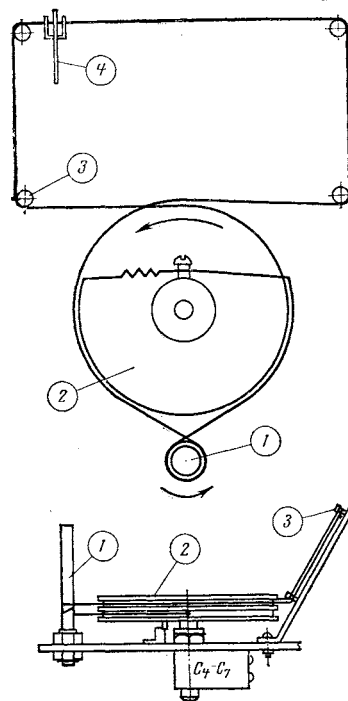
Кинематическая схема верньерного устройства: 1 — ось настройки; 2 — маховик; 3 — направляющая шпилька; 4 — указатель.
